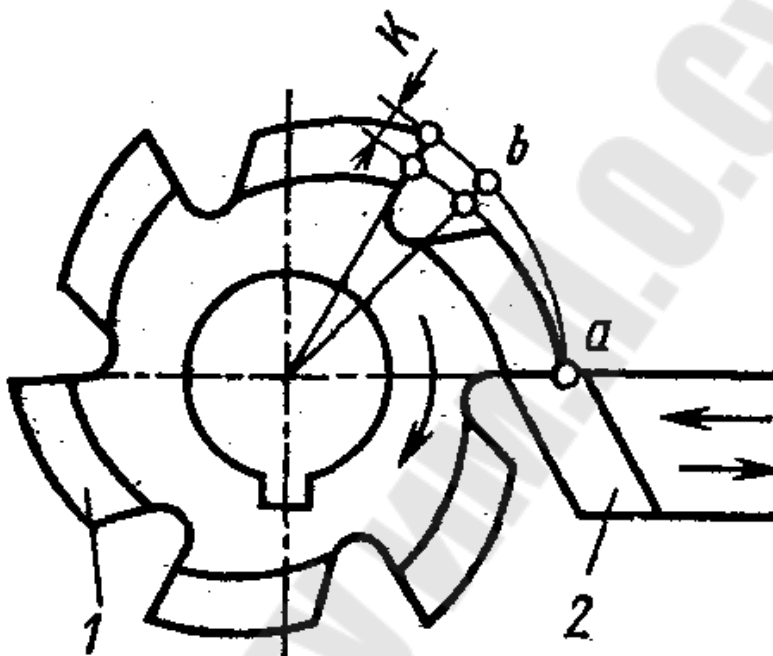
Схема движения резца 2 и изделия 1 при затыловании зуба инструмента на величину затылования К
